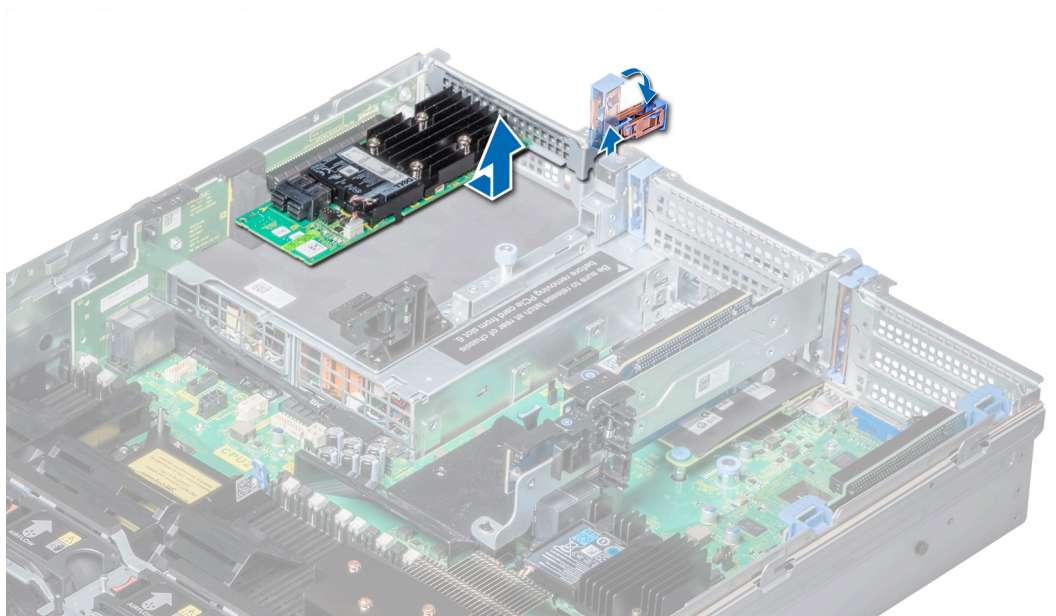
Retrait de la carte d'extension hors de la carte de montage pour cartes d'extension 3
